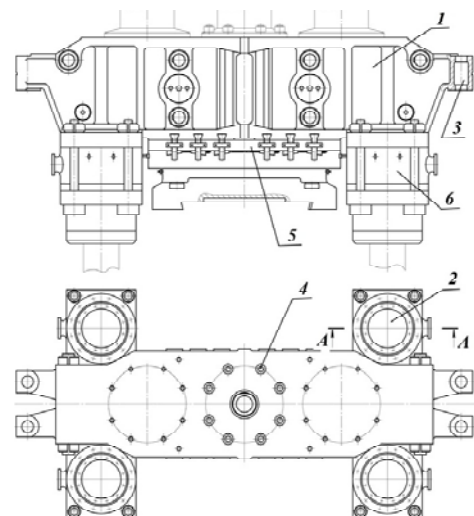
Типовая конструкция подвижной поперечины мощного ковочного гидравлического пресса
